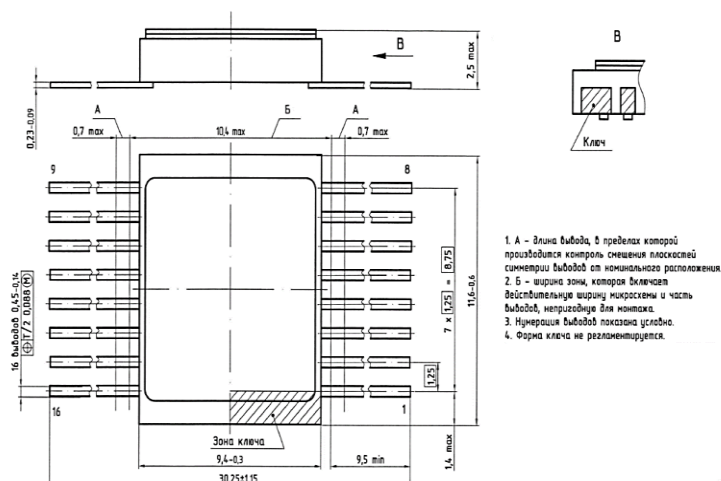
Габаритный чертеж корпуса 402.16-18 (размеры в мм)
